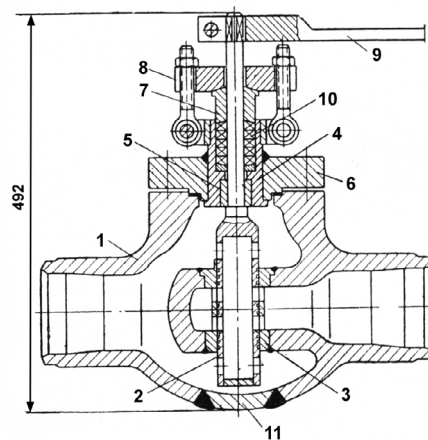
Поворотный регулирующий клапан $D_y 100$:
